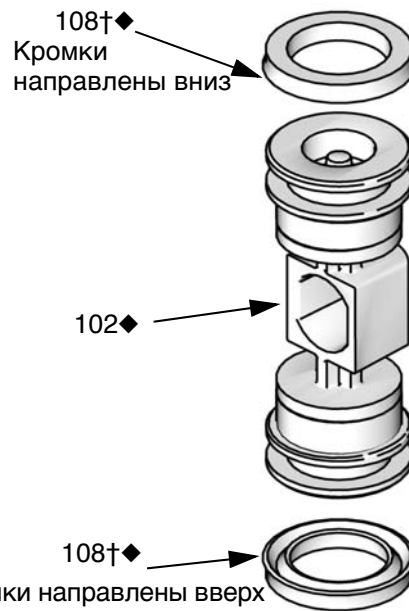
Установка П-образных уплотнительных колец воздушного клапана
